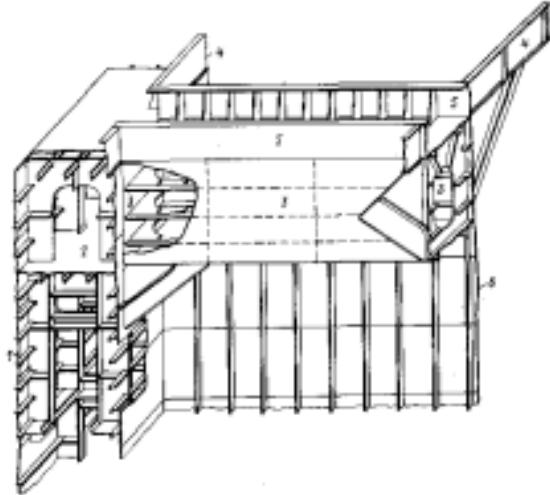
Подпалубный бортовой коридор судна с двойными бортами, соединенный с коридором противоположного борта и поперечными коридорами, исключая палубу продольной переборки
